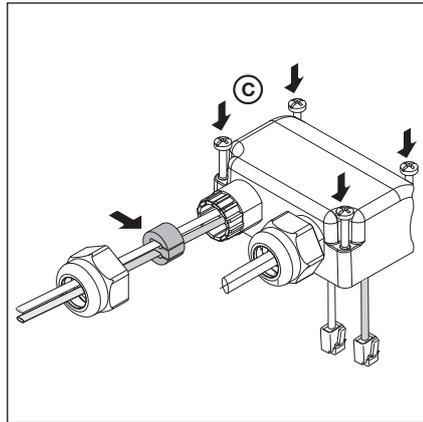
Systemleitung durchführen, Dichtung platzieren
